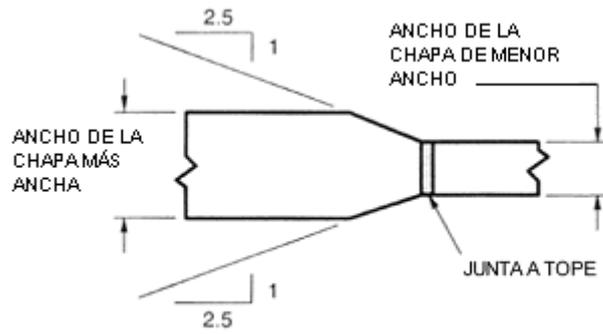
Transición de Anchos (Cargado Estáticamente, Unión No Tubular)
